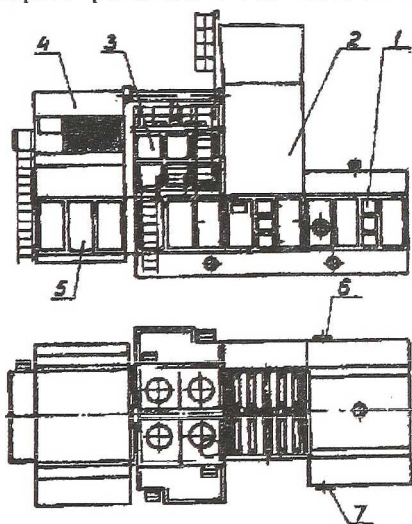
ГПА: 1 - блок турбоагрегата; 2 - устройство выхлопное с шумоглушителем; 3 - блок маслоохладителей; 4 - устройство воздухоочистительное (ВОУ); 5 - камера всасывания; 6 - патрубок всасывающий; 7 - патрубок нагнетательный
